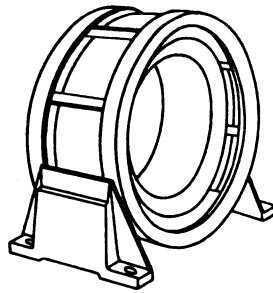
Geschweißtes Motorgehäuse.
